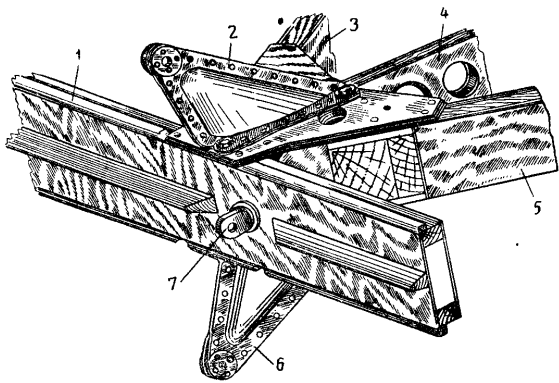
Установка рычагов управления на руле высоты. 1—передний лонжерон руля высоты; 2—верхний рычаг; 3—наклонная нервюра; 4—усиленная нервюра; 5—наклонная нервюра; 6—нижний рычаг; 7—ушковый болт для крепления руля высоты к стабилизатору.
